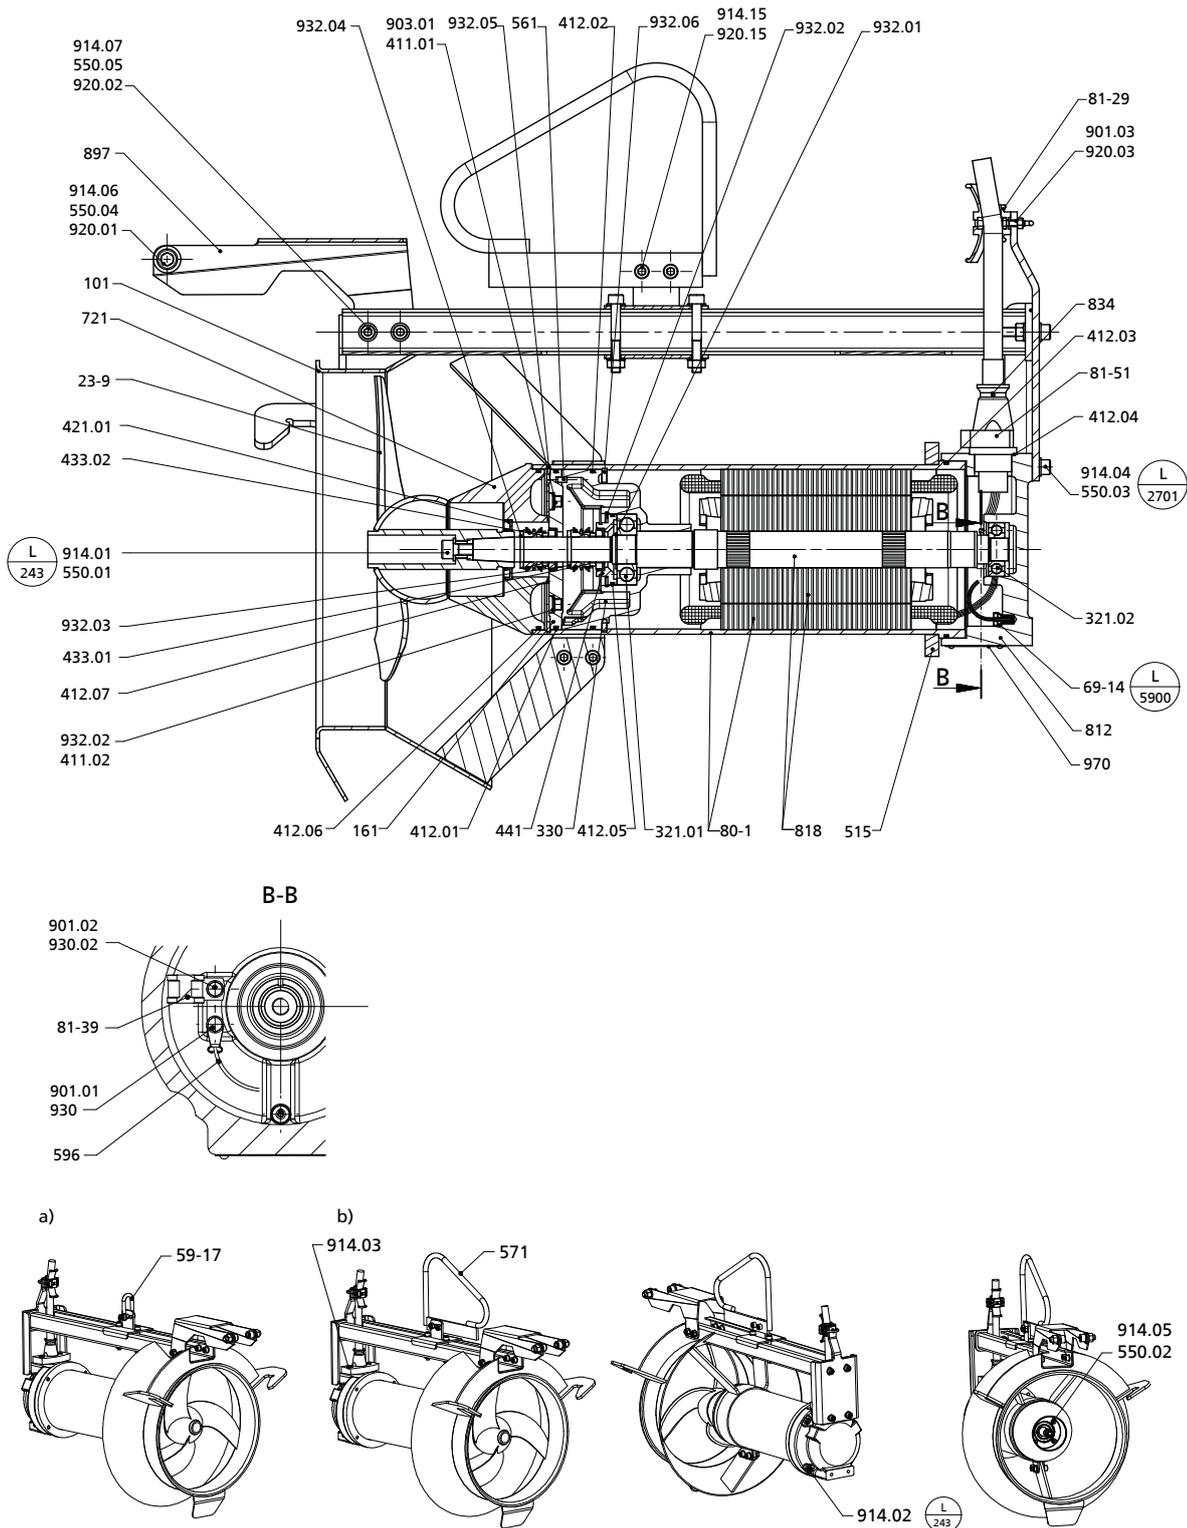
Чертеж общего вида: а) с серьгой б) со скобой (дополнительно)
